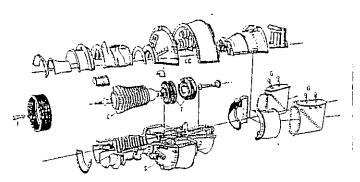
Vista esplose di un impianto con turbina a gus (ORENDA DIVISION). I. Ingresso aria; C. Compressore assiale; CC, Camera di combustione; T. Turbina assiale; S. Semicassa inferiore; G. Uscua zas combusti,
